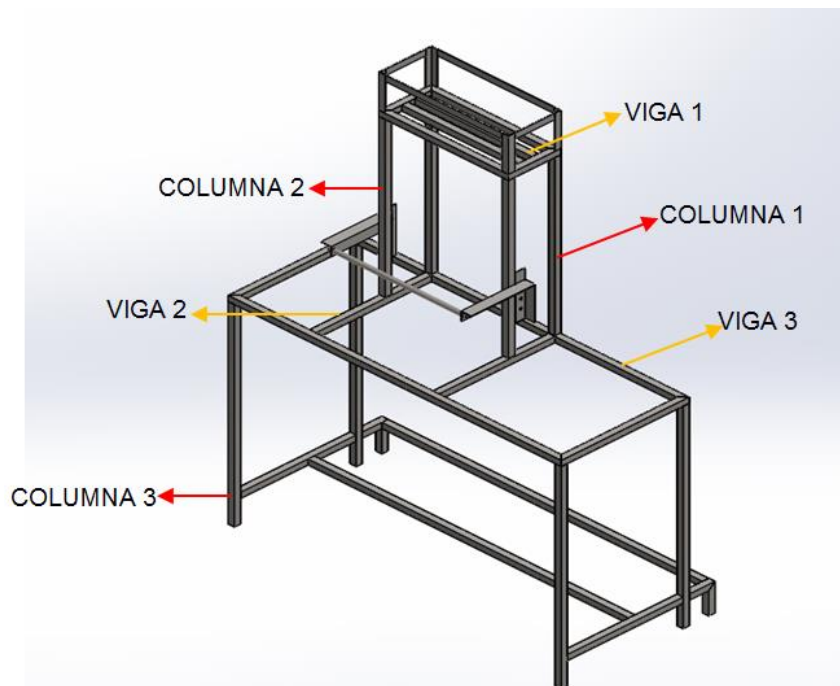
Vigas y columnas para realizar el análisis estructural
